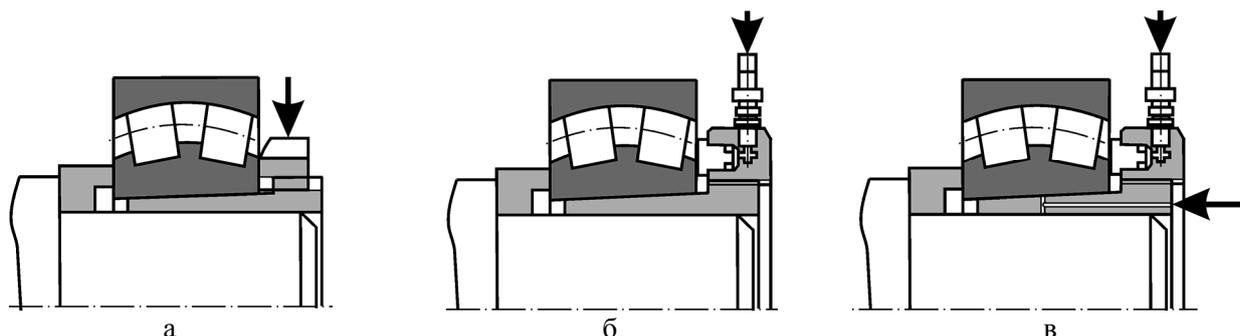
Разборка подшипника со стяжной втулкой с помощью: а – шлицевой гайки и накидного ключа; б – гидравлической гайки; в – гидравлической гайки и подвода масла на сопряженные поверхности подшипника и втулки
